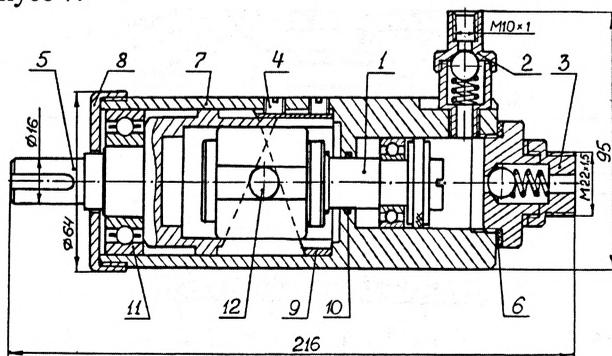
Рабочий чертеж насоса поршневого НП-1
